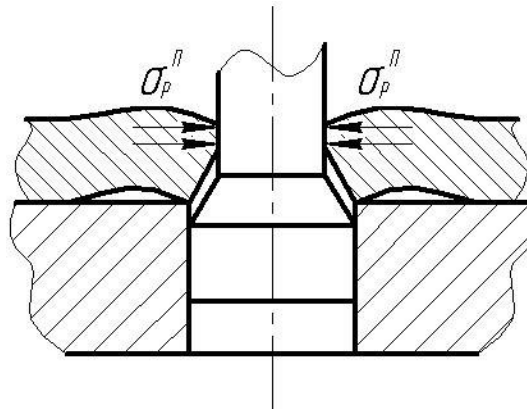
Дія заготовки на інструмент при вирубці без притиску
